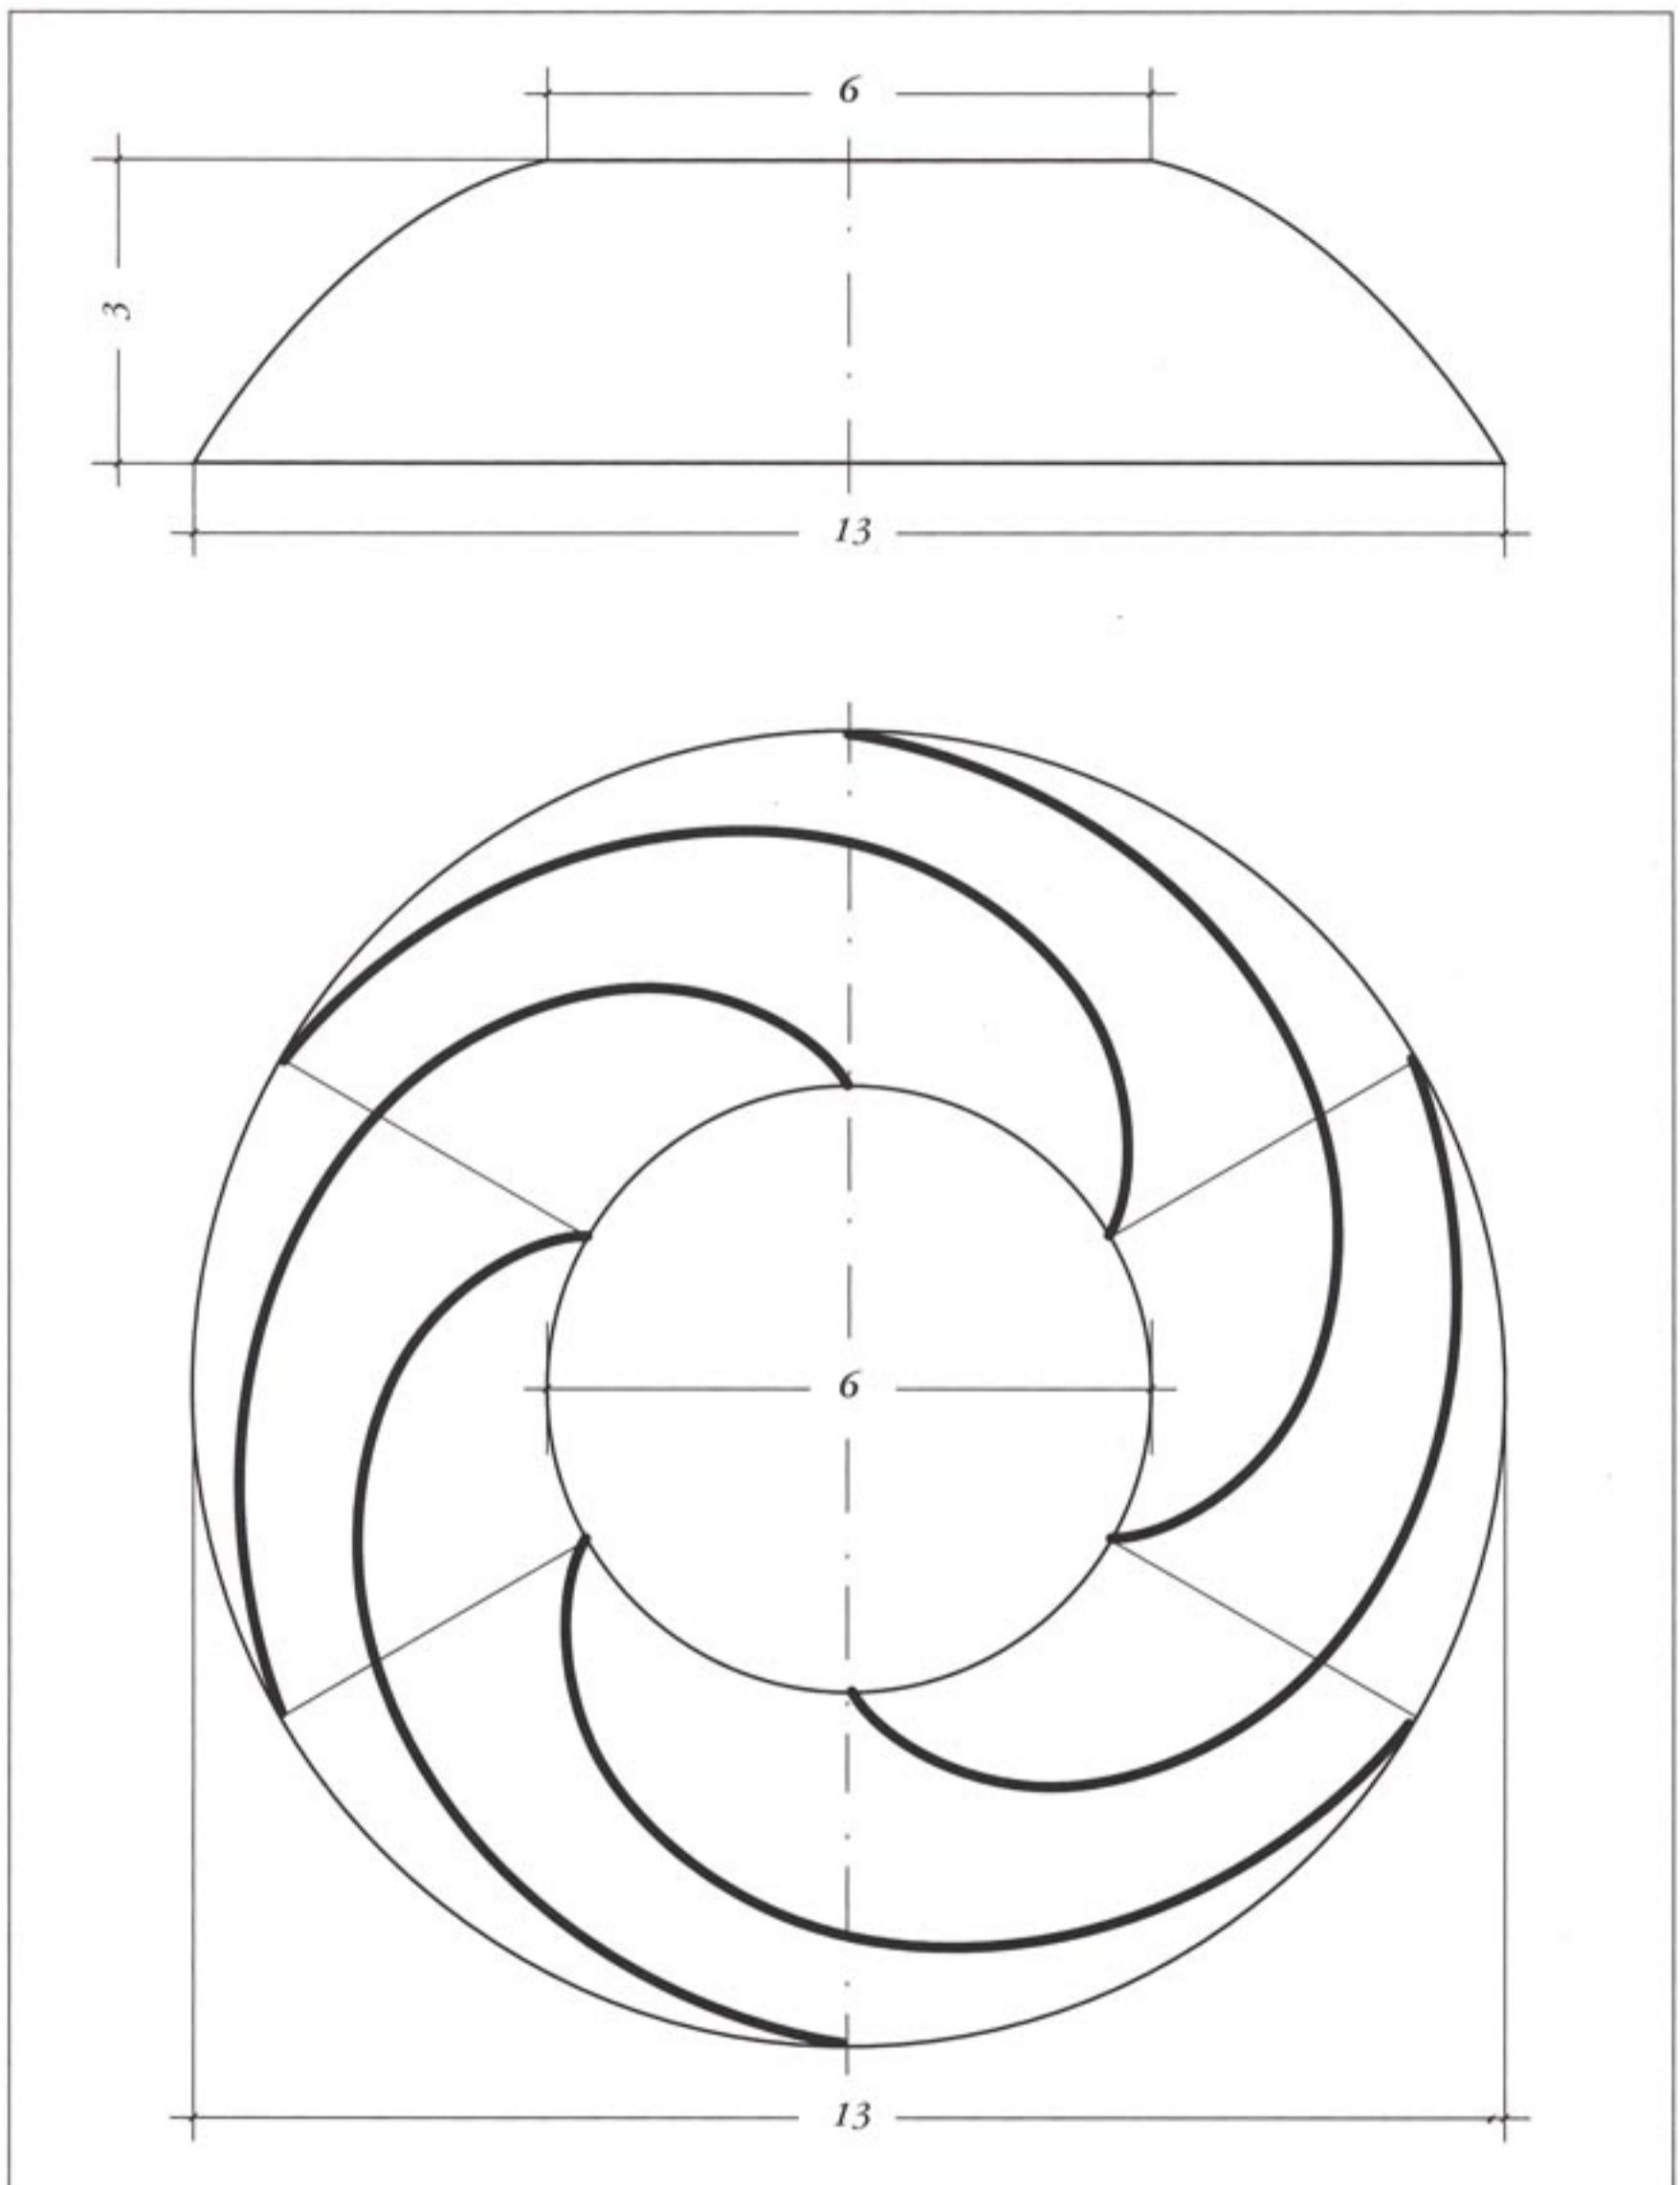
Чертеж и схема разметки основания чаши-вазы к рис. 192
